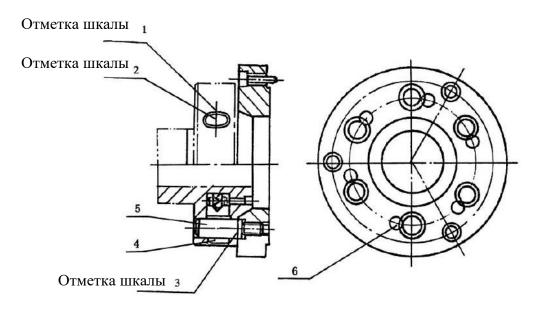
Установка патрона или приводной пластины на шпиндель
